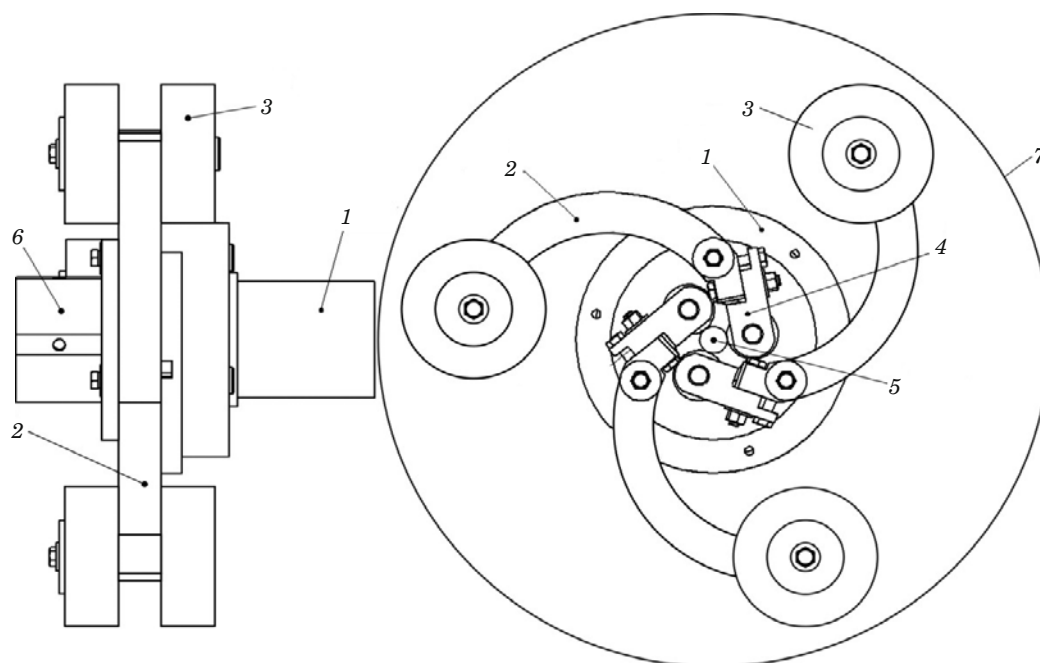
Конструкция центробежного обкатника: 1 — корпус и лекало; 2 — криволинейный рычаг; 3 — груз; 4 — державка с деформирующим роликом; 5 — обкатываемая деталь; 6 — дополнительная опора; 7 — защитный кожух
